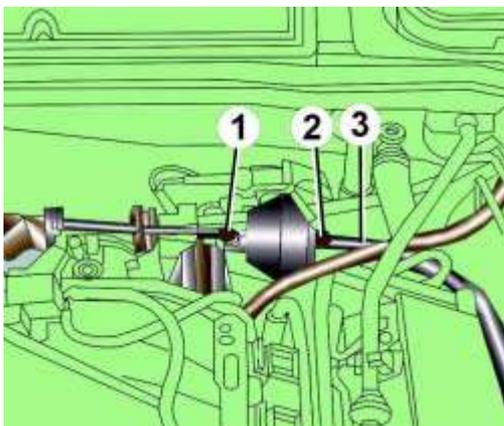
Расположение тяги управления (1), гайки крепления (2) вакуумного блока и вакуумного шланга (3)
